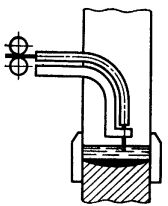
Схема сварки одной электродной проволокой без колебаний
